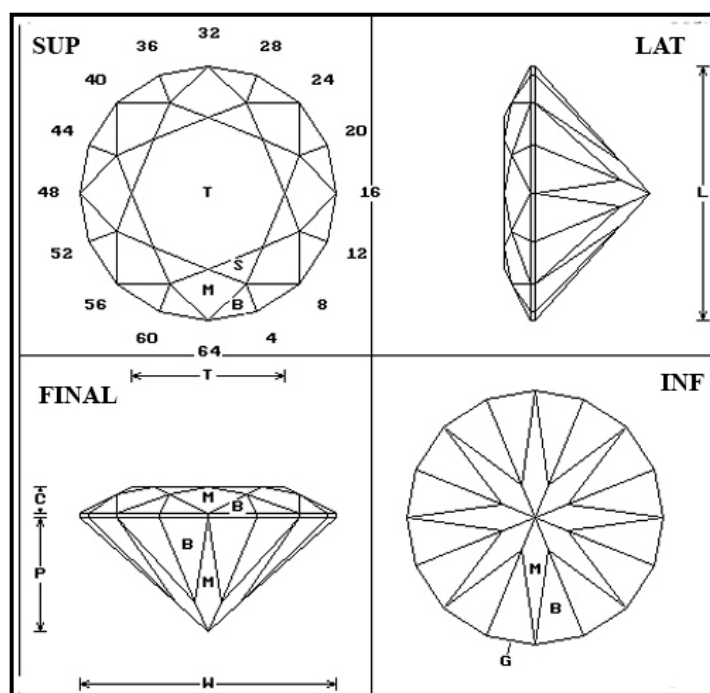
Projeto lapidação redonda brilhante para quartzo (Gemcad 2009).
